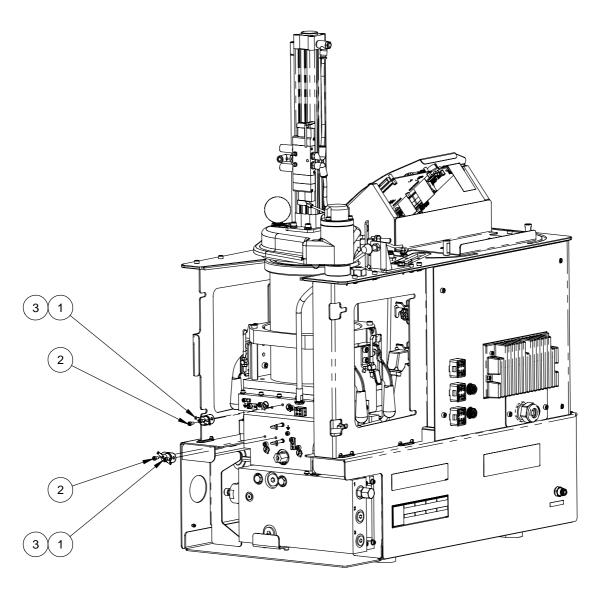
Ersatzteile Baugruppe Thermostat
